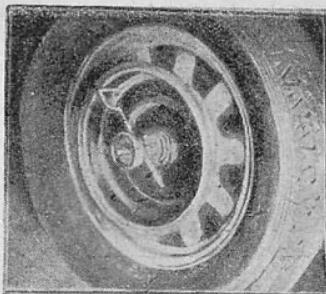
(сверху), 8 (снизу). Установка и регулировка радиуса обработки
